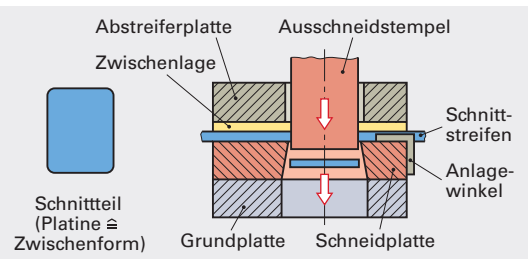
Arbeitsprinzip beim Einverfahrschneidwerkzeug
